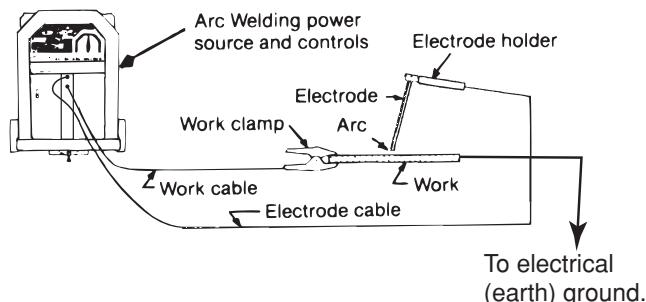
Circuito para la soldadura de arco con electrodo revestido(SMAW).
